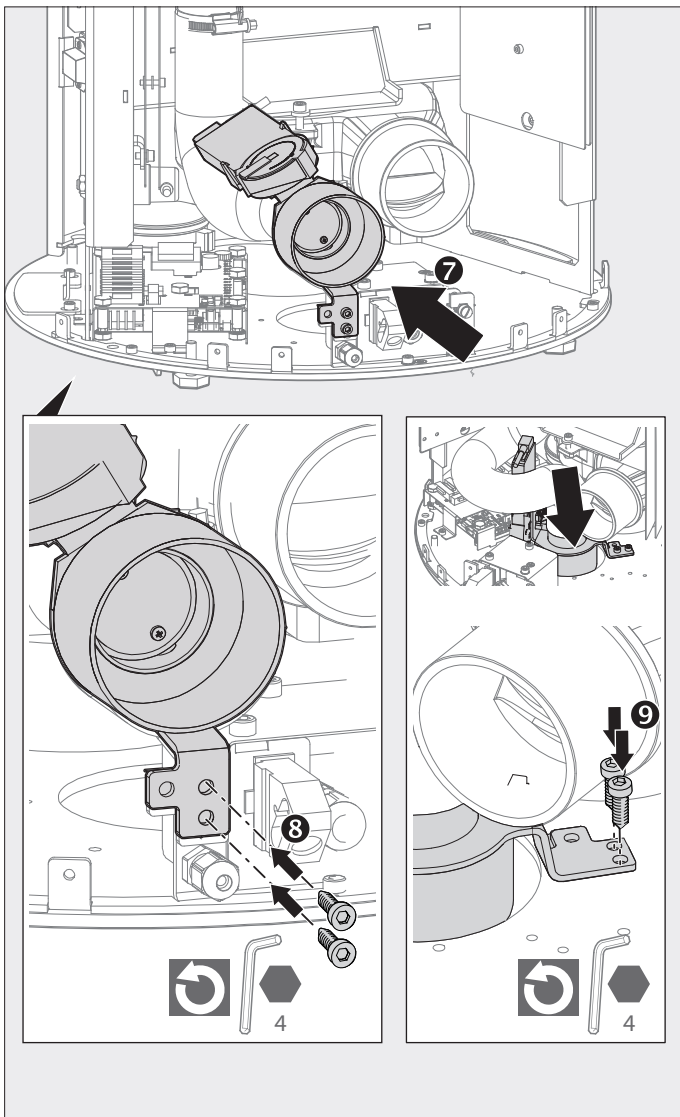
Monter la paroi arrière et le clapet fourni
